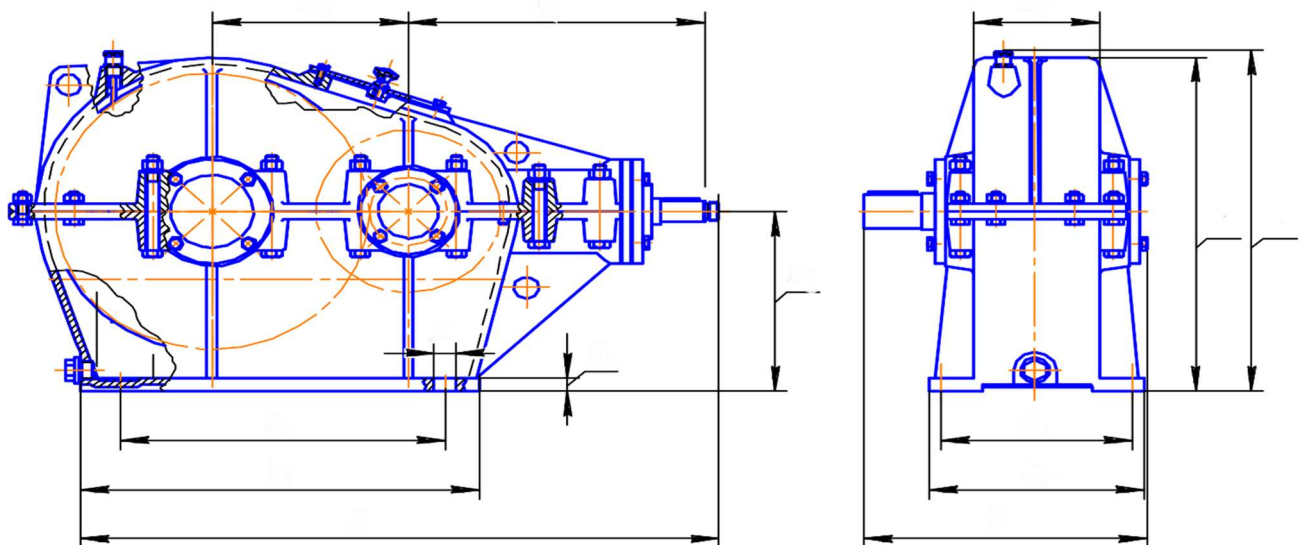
Габаритные и присоединительные размеры коническо-цилиндрического редуктора
